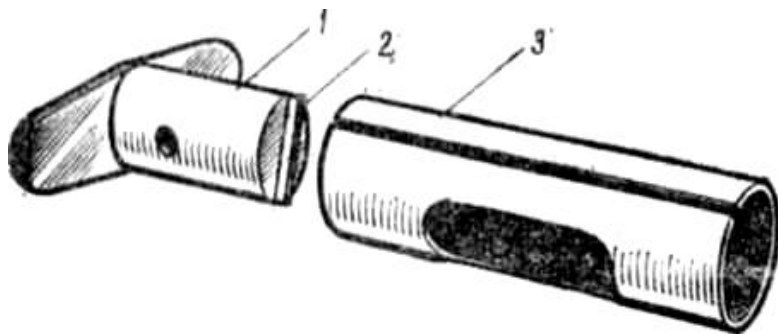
Деталі приладу для зачистки свинцевих циліндрів:
